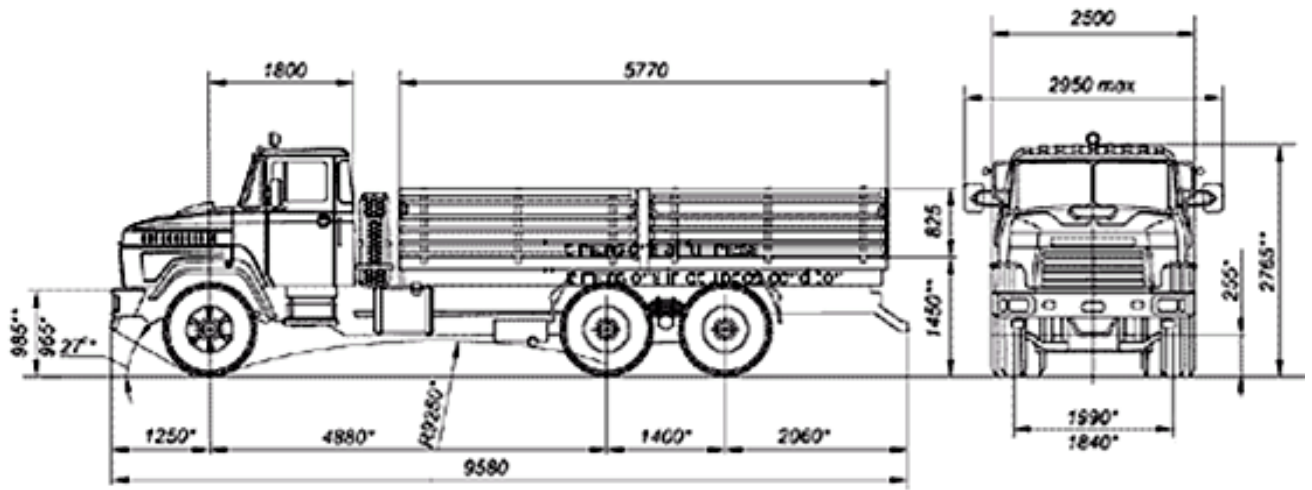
Габаритні розміри КрАЗ-65053
